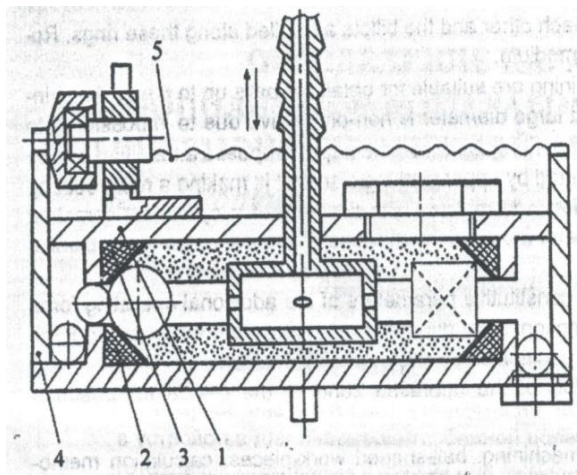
Инструмент для пневмоцентробежной обработки шаровидных деталей из кубиков
